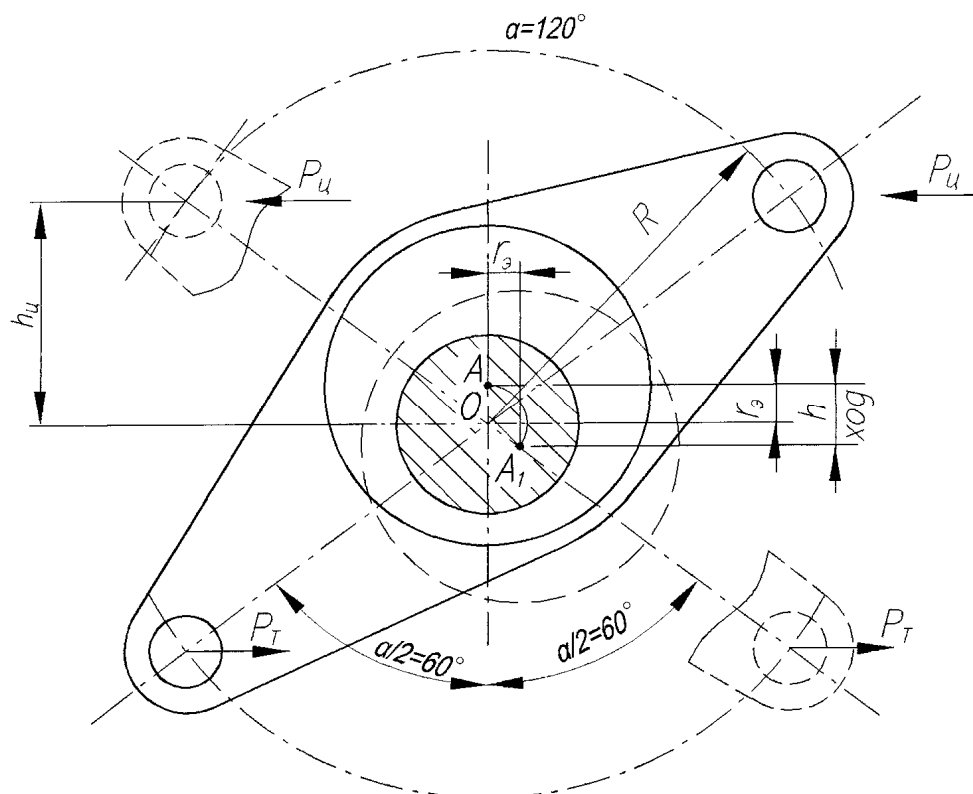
Схема взаимного расположения эксцентриковой втулки и рычагов цилиндра и тяги
